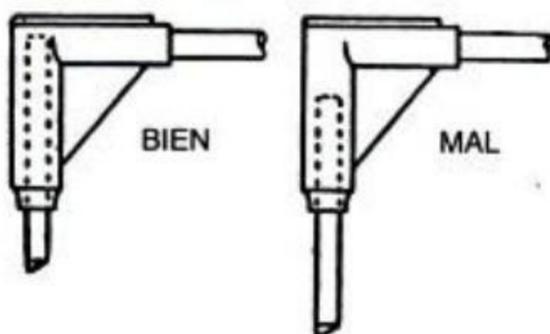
Posición correcta e incorrecta de la punta de un soldador.
